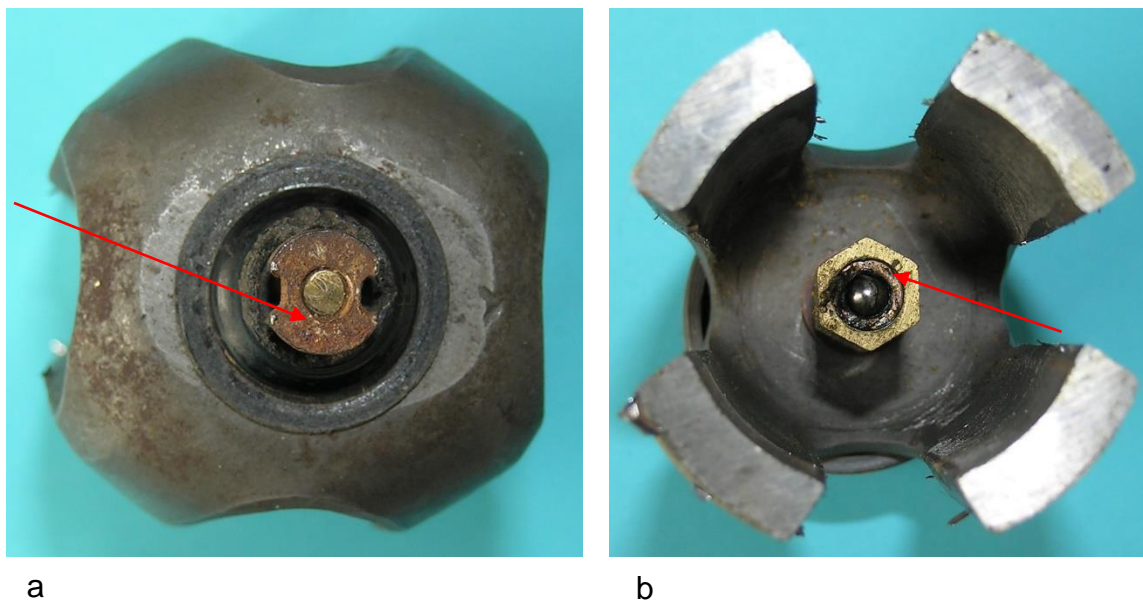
Isolierter Einsatz des Spannung führenden Spurlagers: a) Steckschlüsselmutter, b) Im sechskantigen Messingprofil eingesetztes Gleitlager mit der federnd gelagerten Kugel
